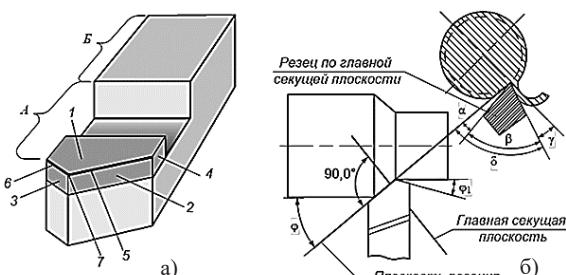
Элементы (а) и главные углы (б) токарного резца: А — режущая часть; Б — стержень; 1 — передняя поверхность; 2 — главная задняя поверхность; 3 — вспомогательная задняя поверхность; 4 — пластина из твердого сплава; 5 — главная режущая кромка; 6 — вспомогательная режущая кромка; 7 — вершина режущей части; γ — главный передний угол; α — главный задний угол; β — угол заострения; δ — угол резания; φ — главный угол в плане; φ₁ — вспомогательный угол в плане
